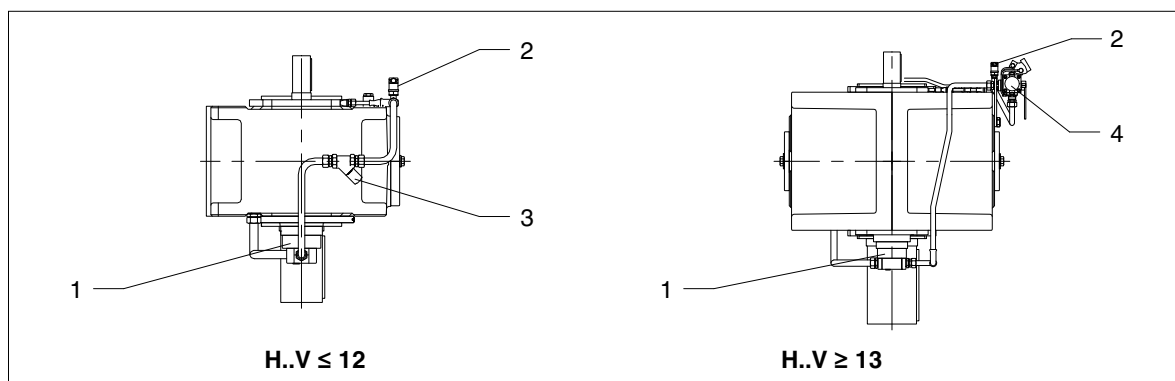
Sistema de alimentação de óleo montado com bomba flangeada no tipo H..V
